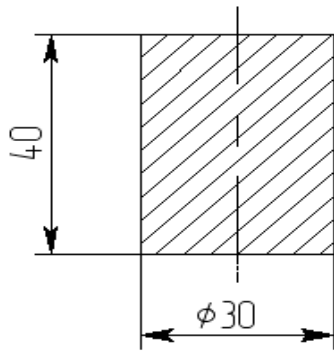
Чертеж детали «сателлит дифференциала»
